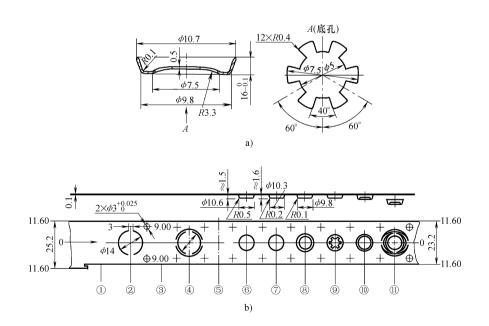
压簧圈级进模 a) 零件图 b) 排样图
